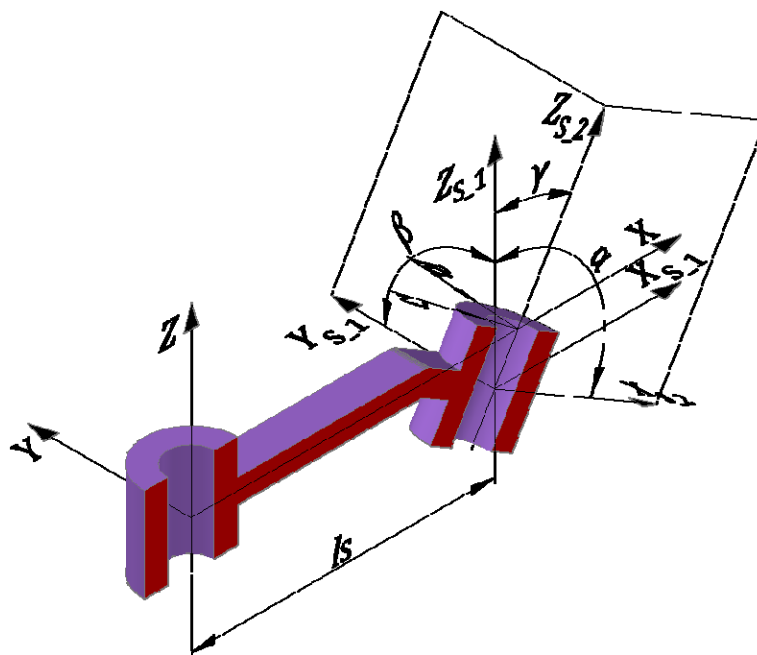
Розрахункова схема рухомої ланки (шатуна) з похилою циліндричною головкою
